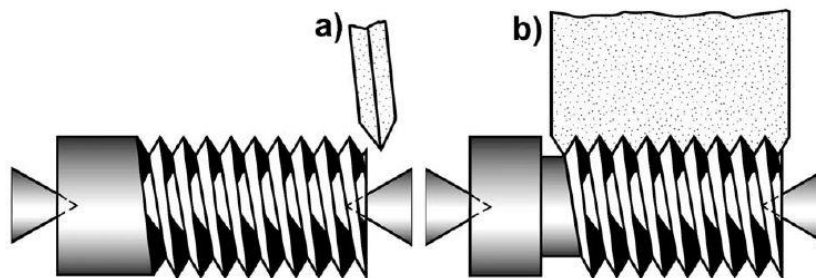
Metody frézování závitů [9]: a) kotoučová fréza, b) hřebenová válcová nástrčná fréza.
